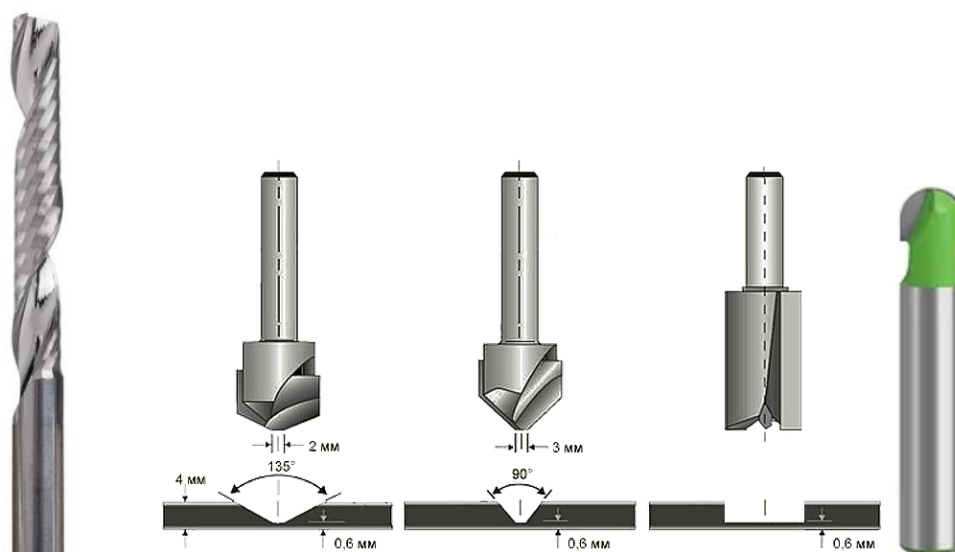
Інструменти для фрезерування листового композиту
